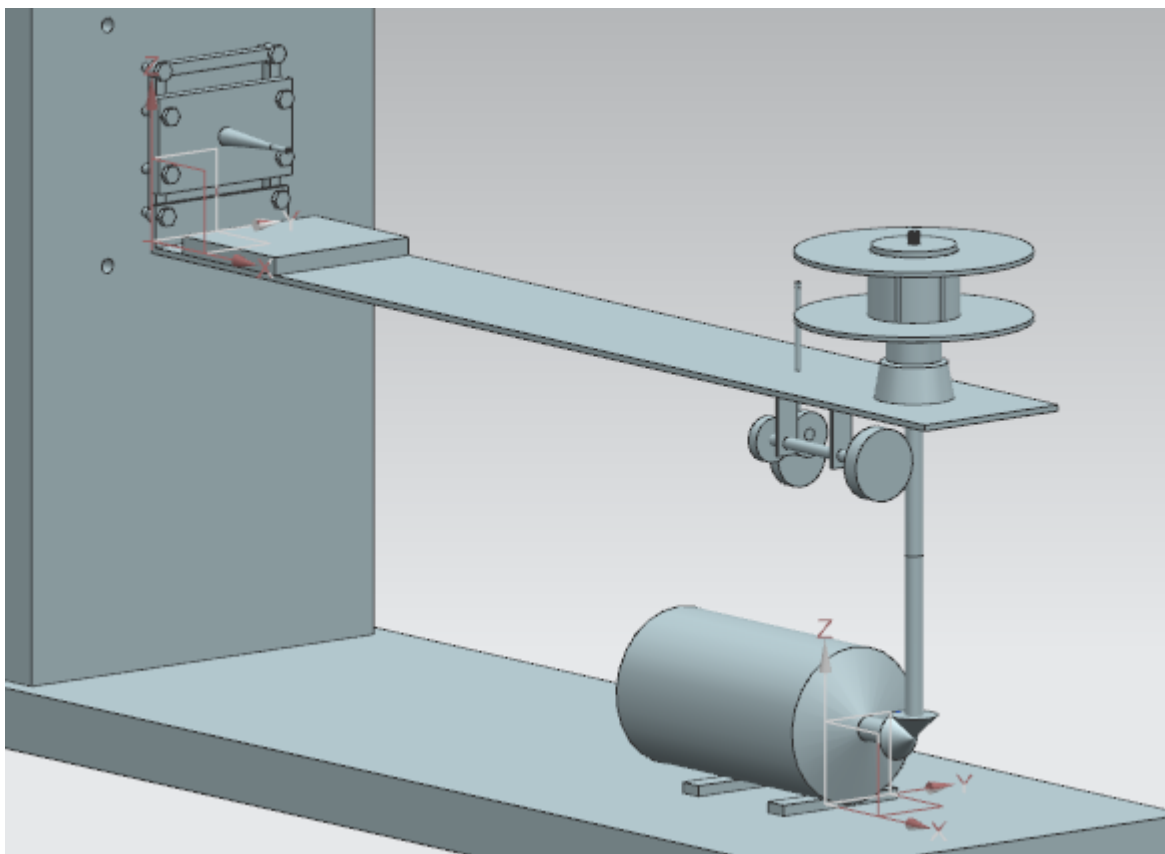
Конструкция для получения расходного материала для 3D-принтера и намотки её на катушку.
